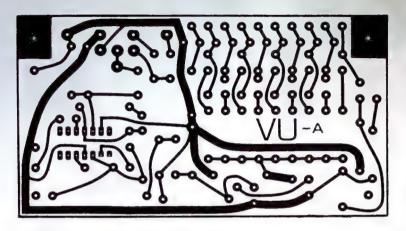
Die Abmessungen des Prints wurden für das Modulsystem passend gewählt.
